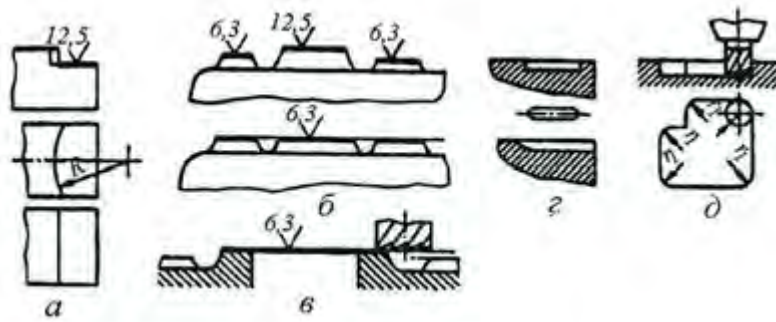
Приклади поліпшення технологічності поверхонь деталей машин, оброблюваних на фрезерних верстатах
